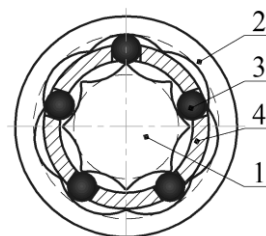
Зубчатая передача с промежуточными телами качения и параллельными осями: 1) зубчатое колесо; 2) зубчатое колесо; 3) промежуточное тела качения; 4) сепаратор
